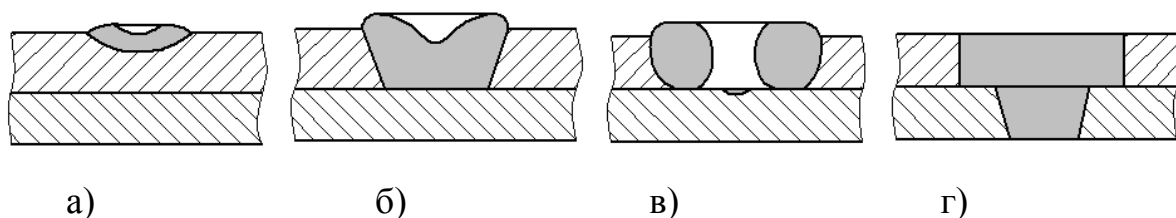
Фазы формирования сварной точки на сплаве алюминия [7]
